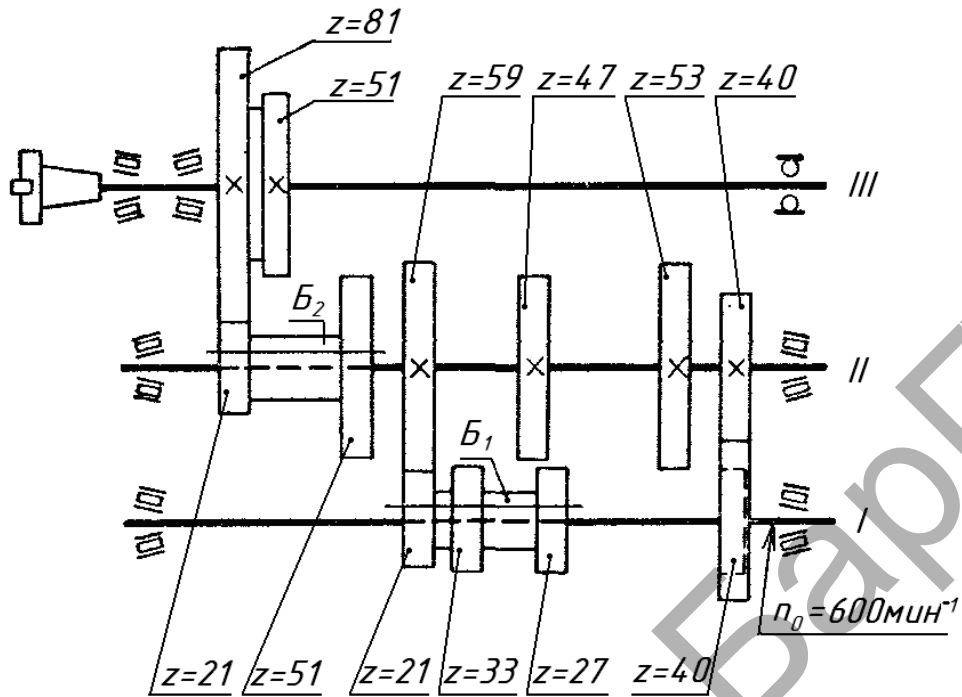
Коробка скоростей с передвижными блоками колес
